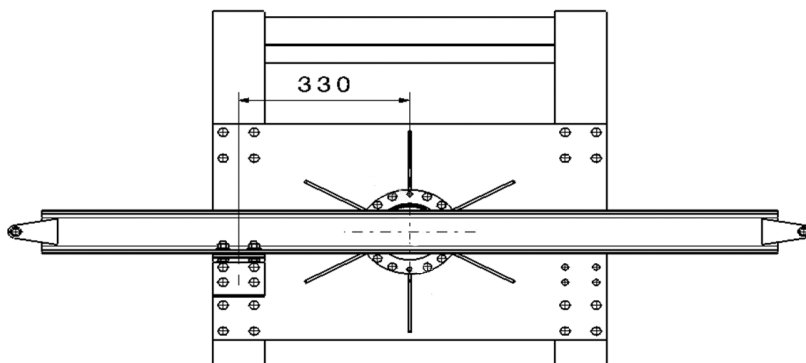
Zeichnung der Seite der Blattwurzel Torsionsmechanismus, Draufsicht.
